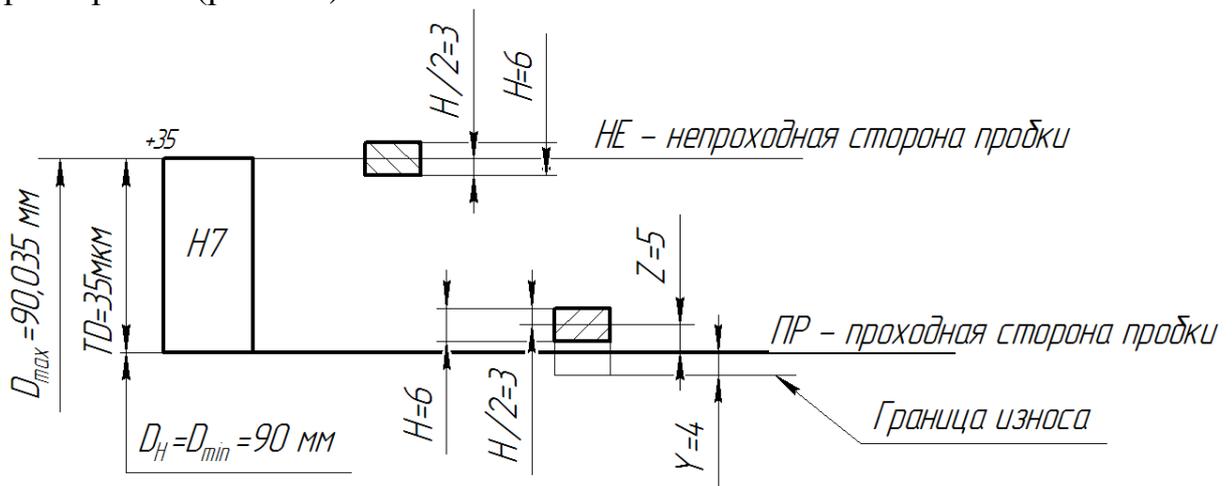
Схема полей допусков калибра-пробки
